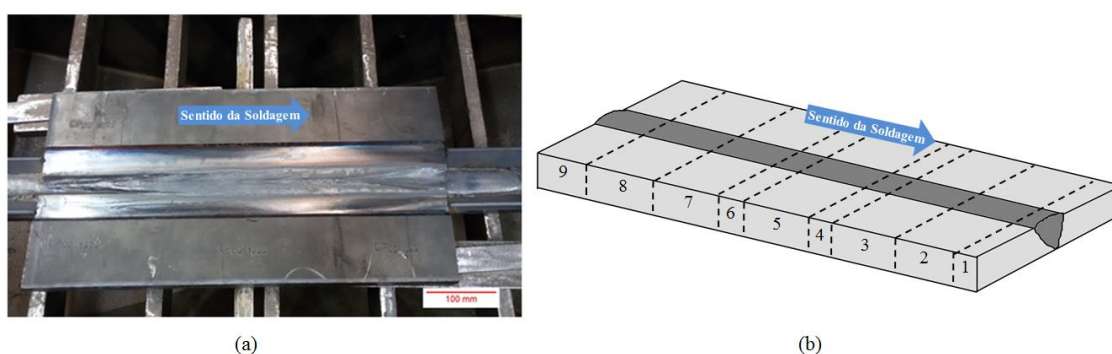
a) chapa soldada; b) Identificação das regiões de corte das chapas para usinagem de corpos de prova de tração e fadiga.
